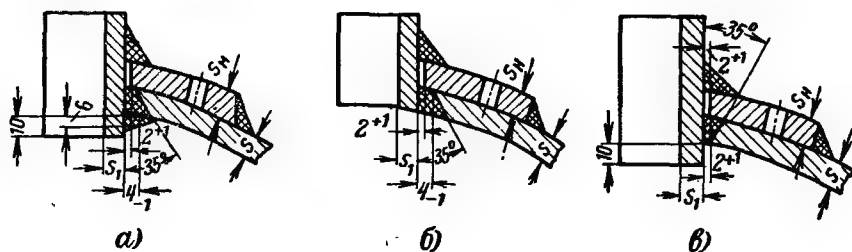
Варианты узла приварки усиливающей накладки к корпусу сосуда и патрубку.
